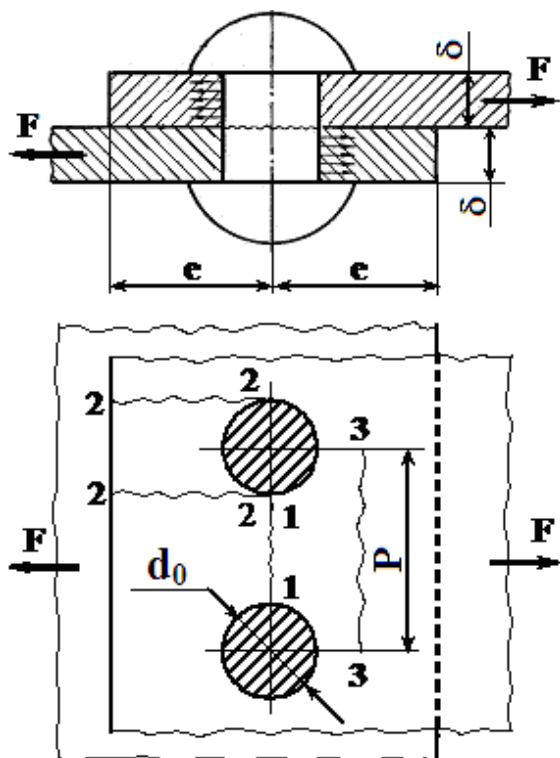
Розрахункова схема заклепкового з'єднання
